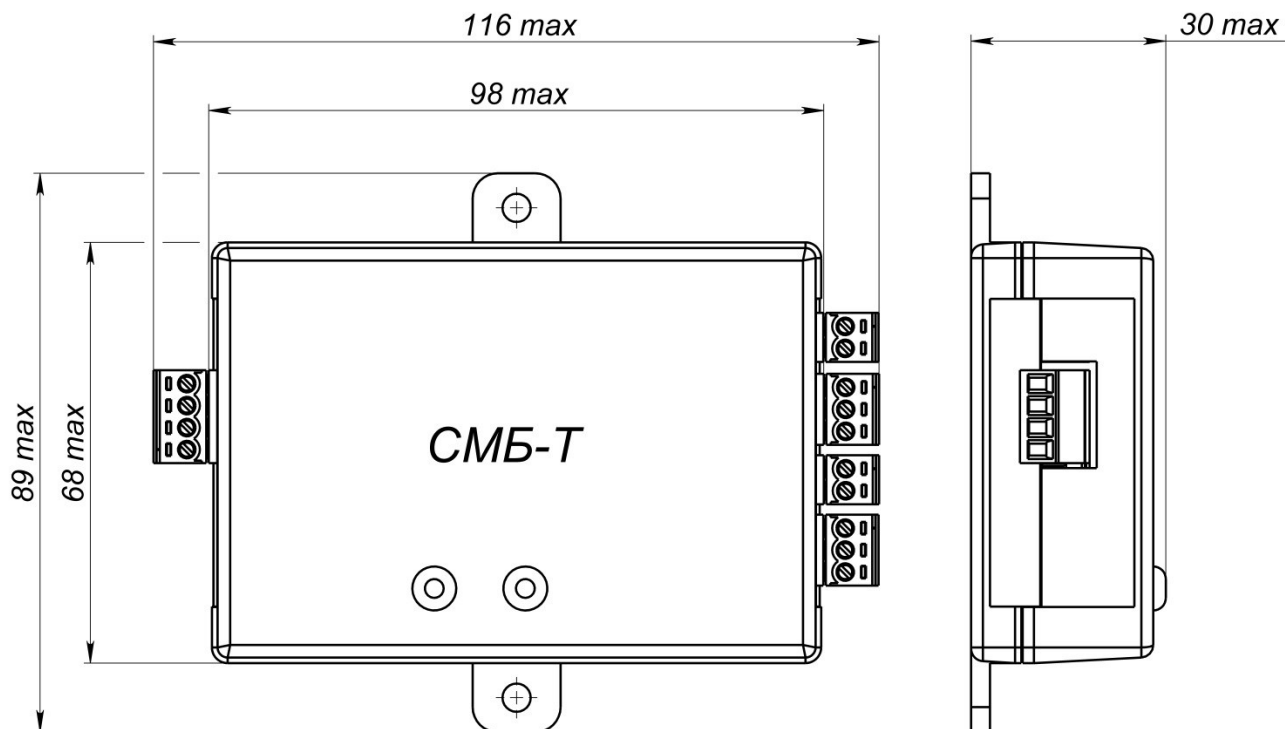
Габаритный чертеж модуля СМБ-Т
